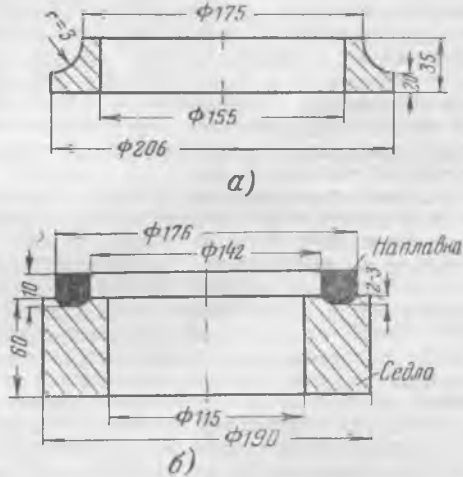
Заготовки седла вентиля для варки в корпус (а) и уплотнительного кольца для наплавки (б).
